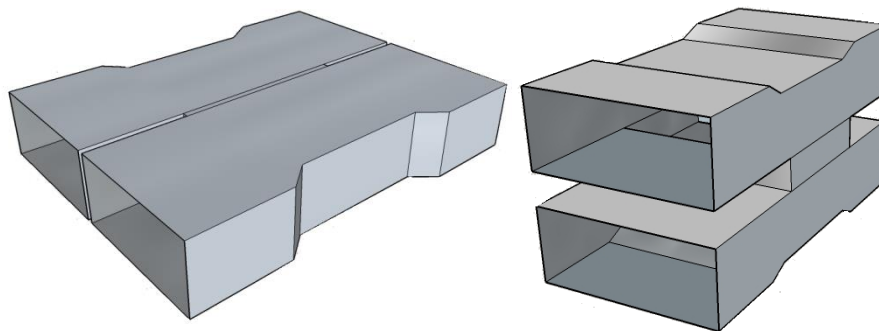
Acoplador Riblet con geometría en plano H (izquierda) y en plano E (derecha)
